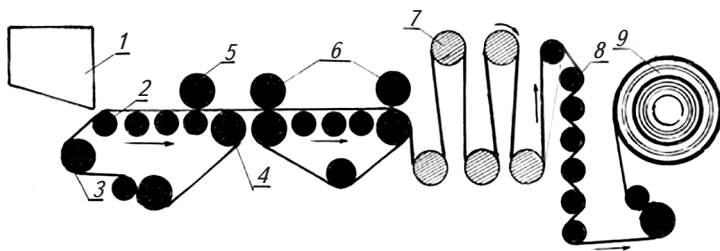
Схема папероробної машини: 1 — напірний бак; 2 — сітка;
